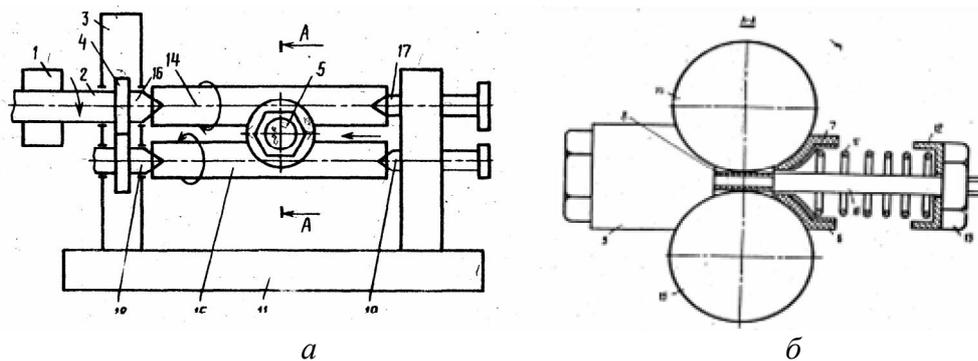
Общий вид устройства –(а) и разрез по линии А-А: 1 – механизм вращения; 2 – вал; 3 – корпус; 4 – дополнительный механизм вращения; 5 – натирающий узел; 6 – наконечник; 7 – чехол; 8 – тампон; 9 – обойма; 10 – ось; 11 – пружина; 12 – шайба; 13 – гайка; 14,15 – обрабатываемые детали; 16-19 – центры
